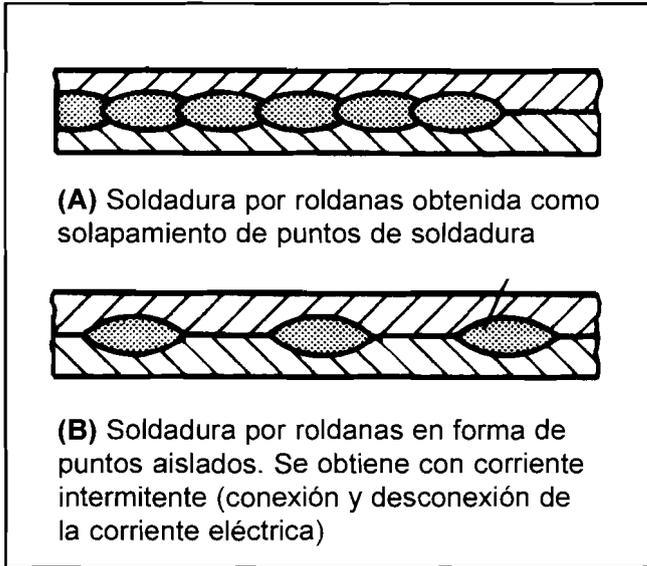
SOLDADURAS POR ROLDANAS
